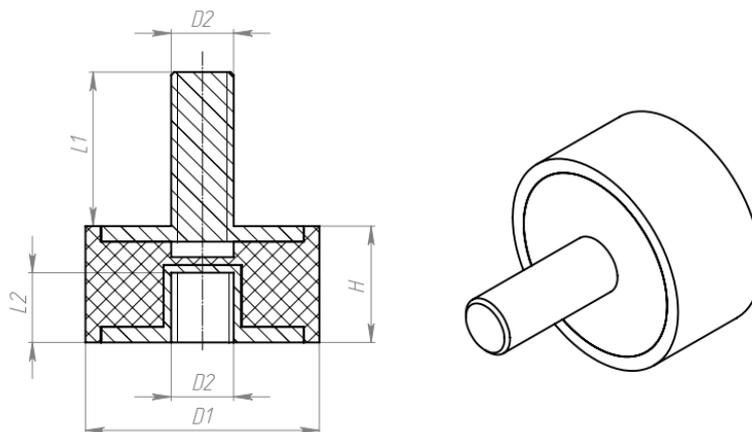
Внешний вид и основные размеры виброопор RVI
